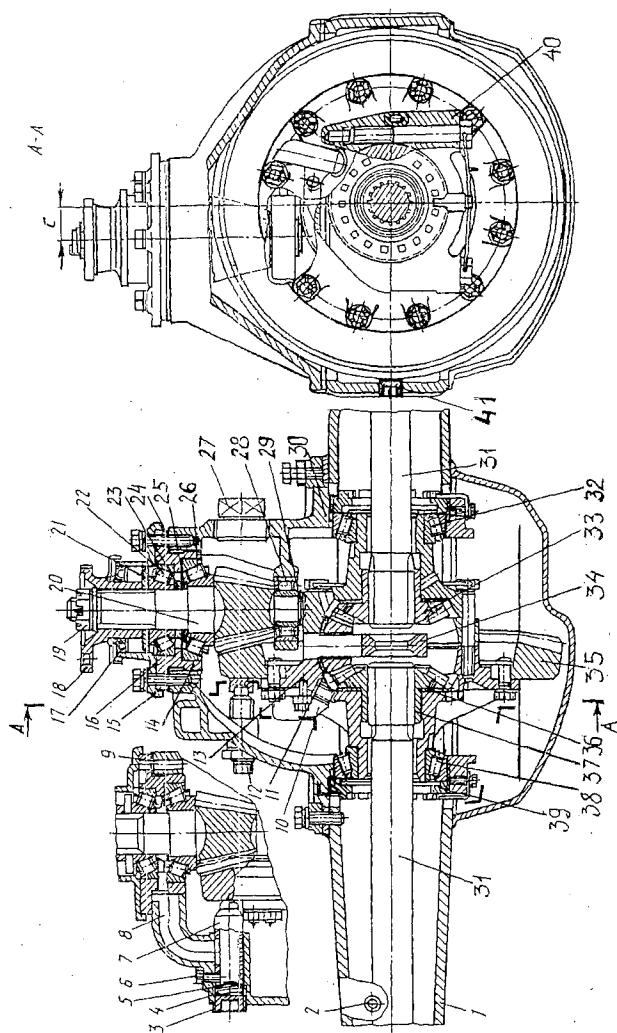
Одинарная гипoidная главная передача автомобиля ГАЗ-3307:
